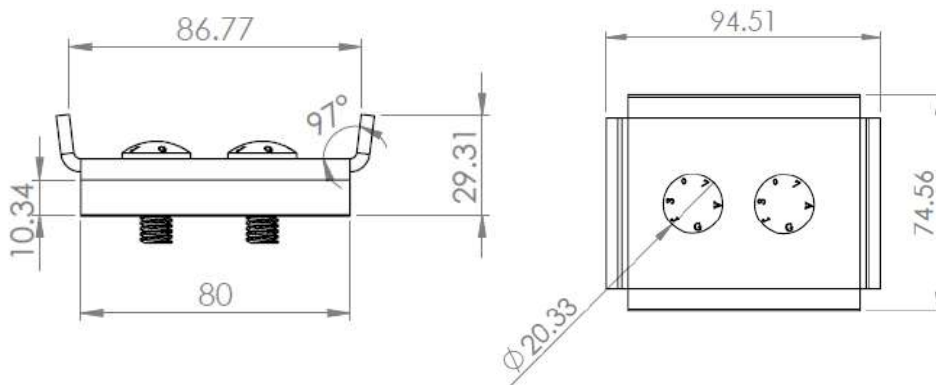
Vistas y dimensiones de componentes del código HTS-2F
